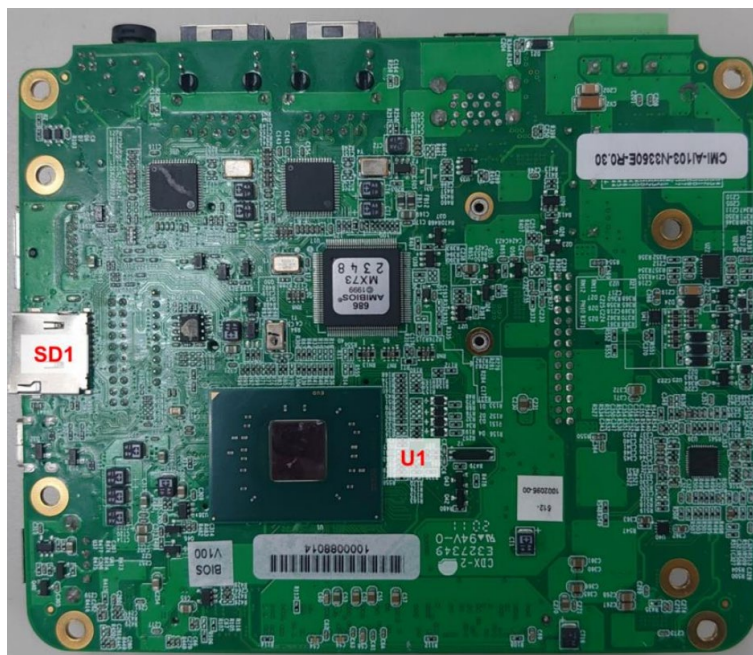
CMI-AI103 - Anschlüsse und Jumper – Untersicht
